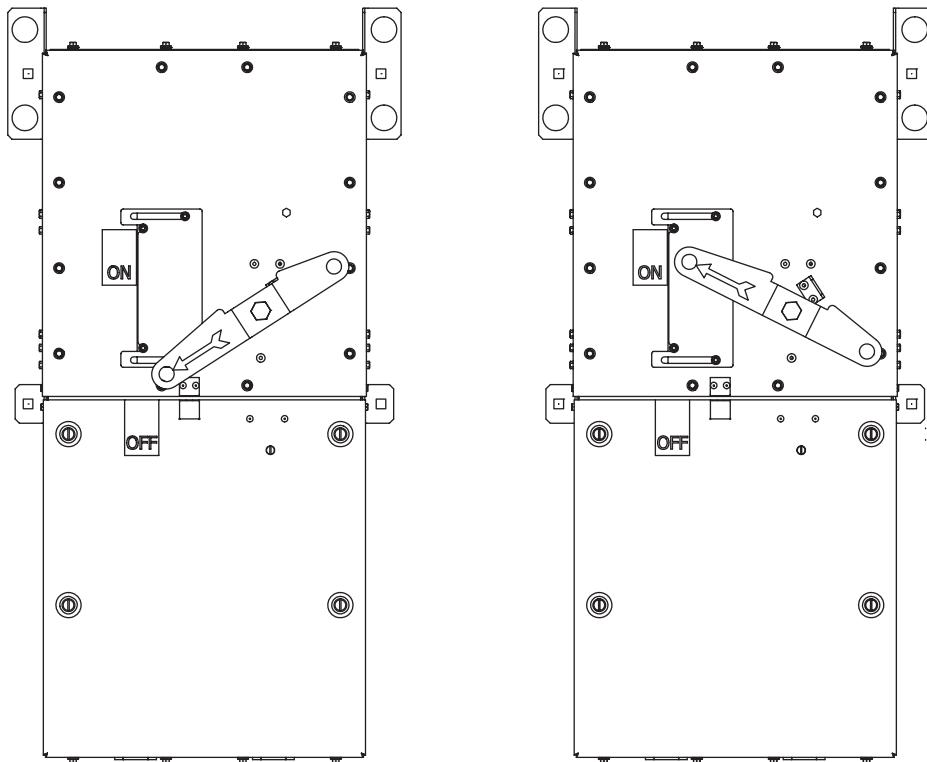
Essai avant installation, unités enfichables installées verticalement
